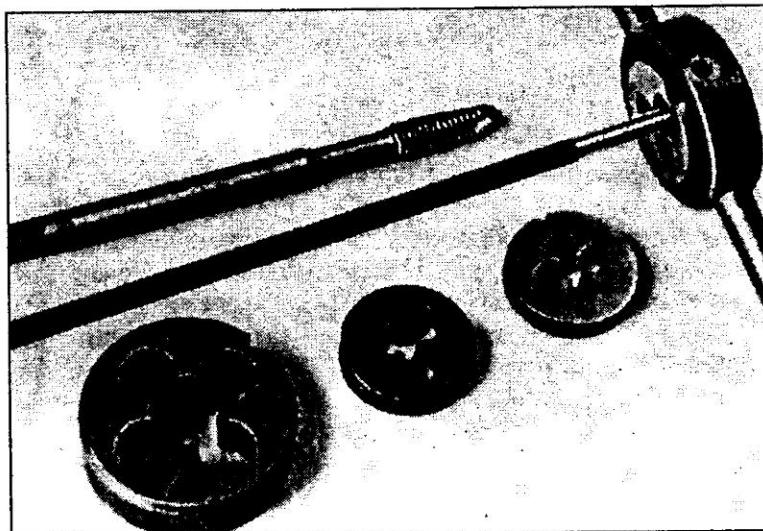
Инструмент для нарезания резьбы: вверху — мётчик, им нарезается внутренняя резьба (обычно используются два метчика — для предварительной и чистовой нарезки); в середине — плашкодержатель с плашкой и стержень с нарезаемой резьбой; внизу — плашки различных типоразмеров для нарезания резьбы на валах
